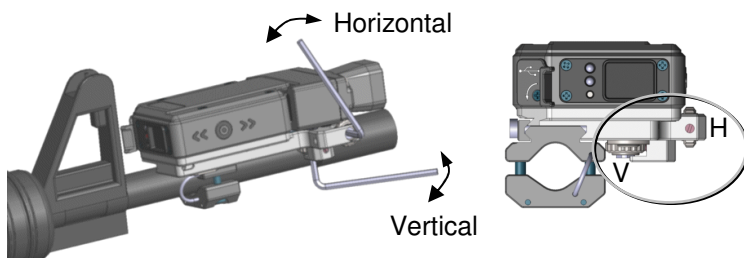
Cereo mecánico – Ajustes (en posición de montaje defecto)
